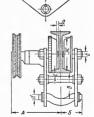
Двухкатковая кошка с ручным механизмом перепвижения.
